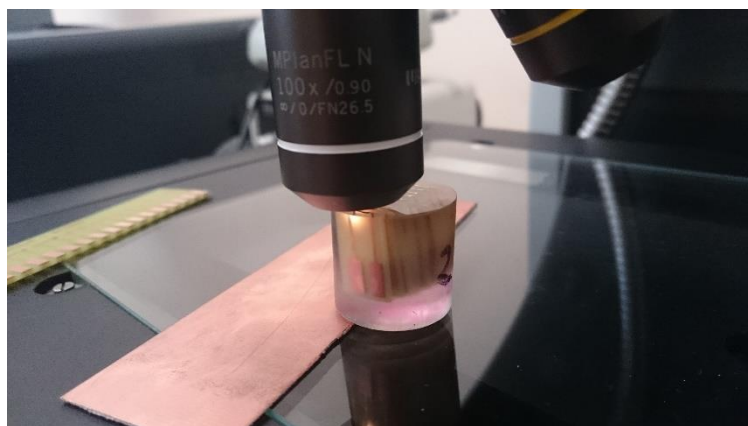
testované součástky a DPS, povrchová úprava - Cu
